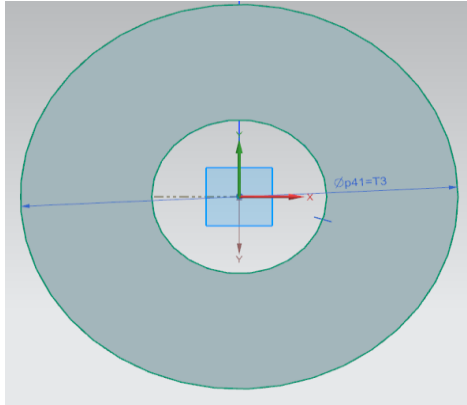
Замена размеров формулами для детали «GAUKA2»
